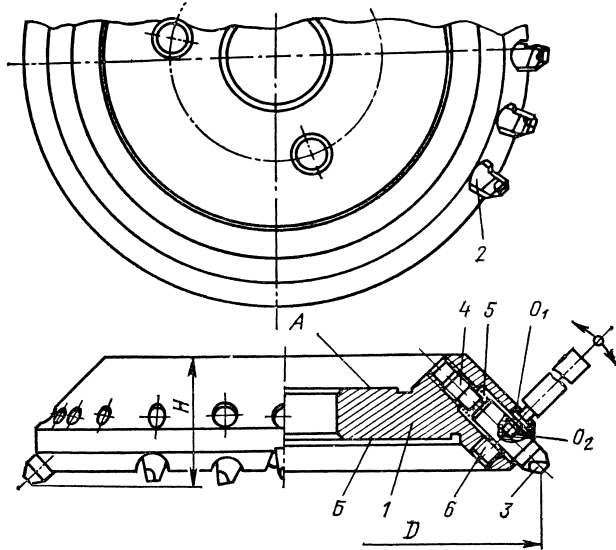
Фреза насадная ступенчатая регулируемая со вставными ножами из сверхтвердых материалов (А, Б — опорные торцы; O_1 , O_2 — оси отверстий в корпусе и ноже):
